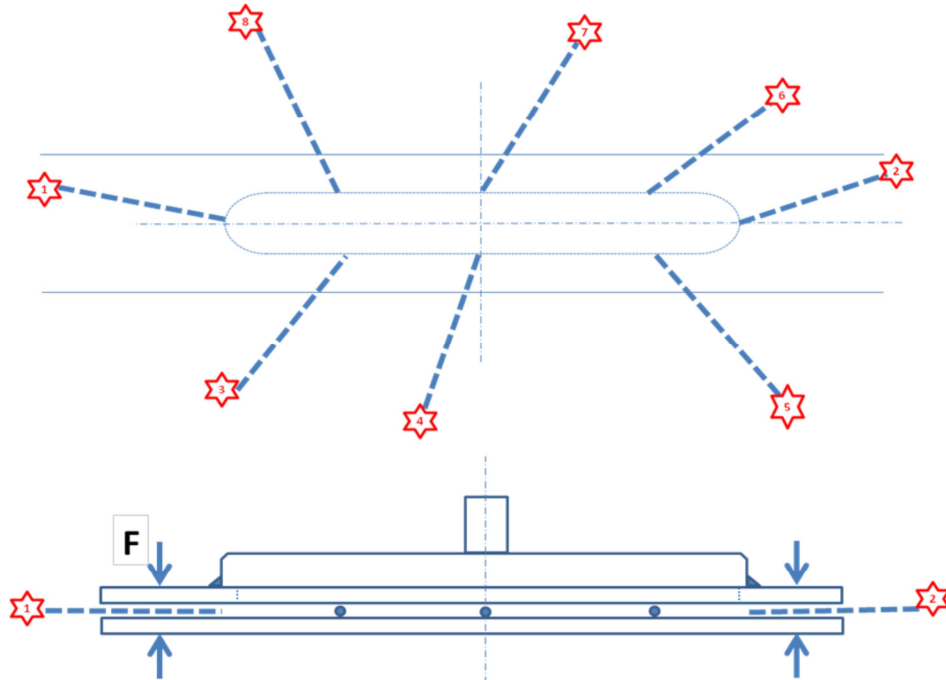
Identificazione saldature iniziali / *First welds identification
